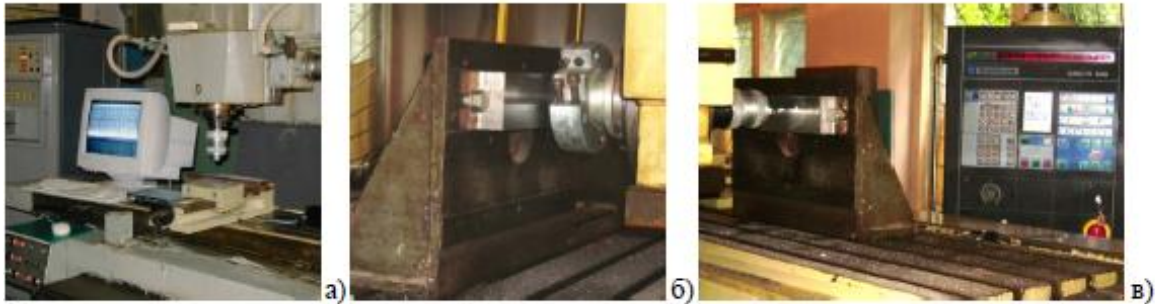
Алмазне вигладжування деталей на верстаті 6P13Ф3(а); торцеве фрезерування (б) та алмазне вигладжування (в) деталей на верстаті FQW-400 із системою ЧПУ CNC-H 646
